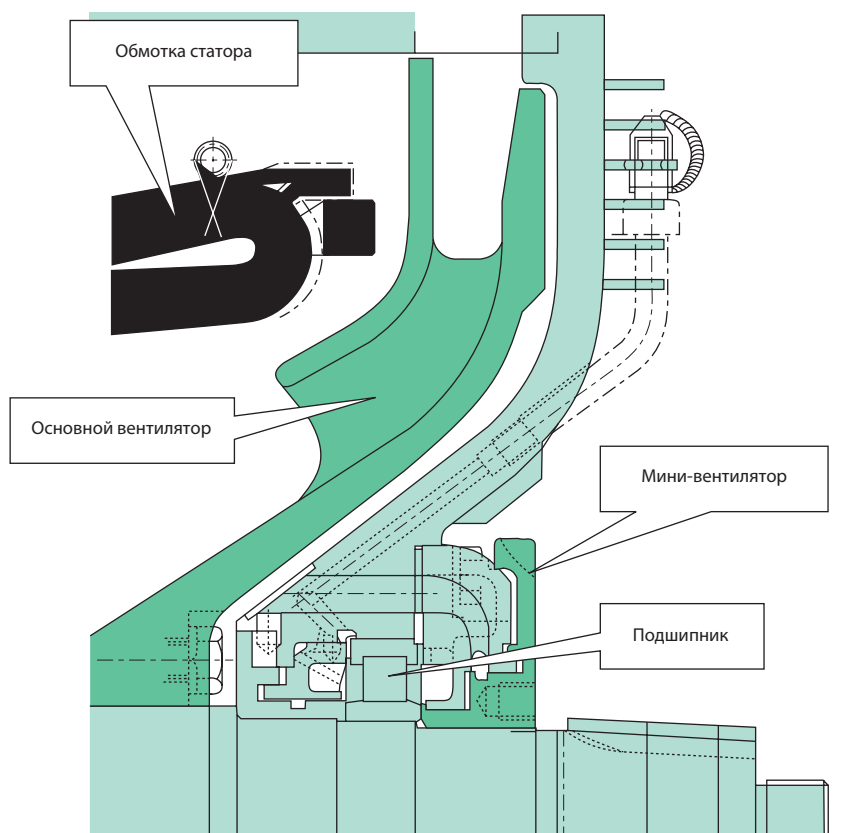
Конструкция подшипникового узла со стороны тягового редуктора и вентилятора
